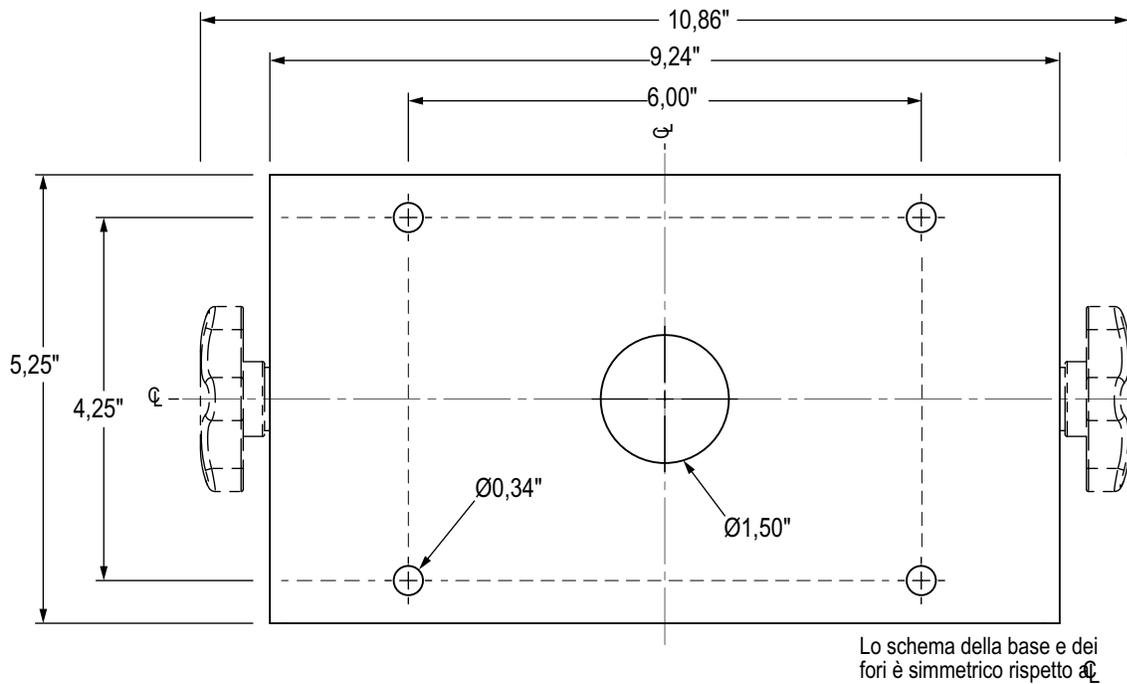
Dimensioni dei fori del supporto inclinabile dell'involucro universale
